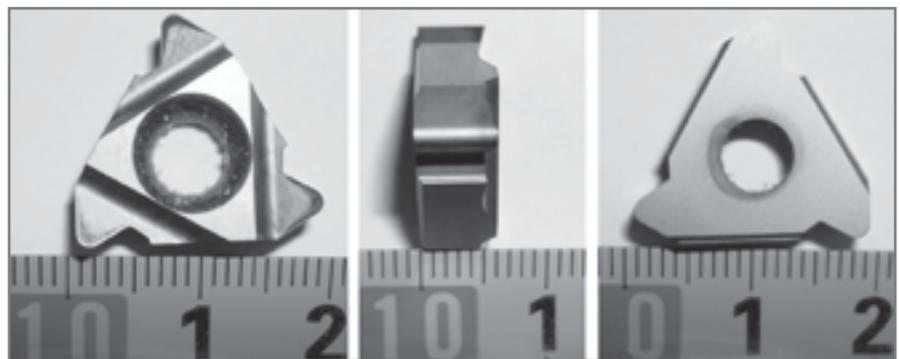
Пластина: а – фронтальный вид, б – вид слева; в – вид снизу
